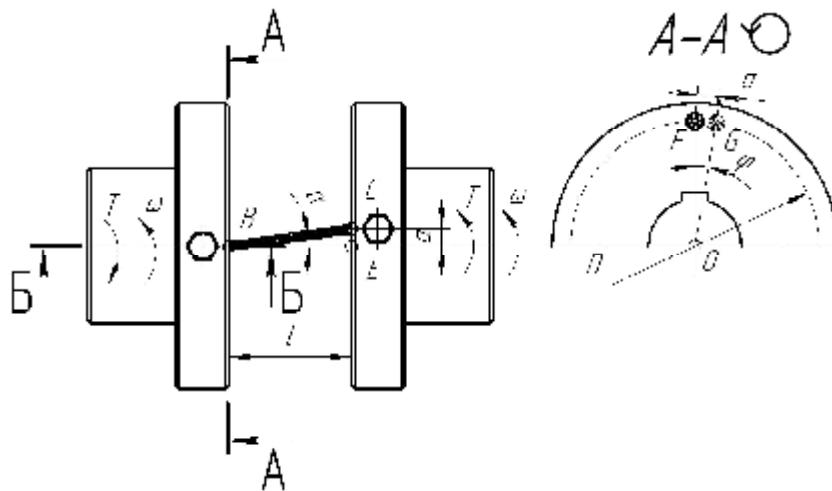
Розрахункова схема муфти з осью паралельною установкою канатів прямолинійної форми
